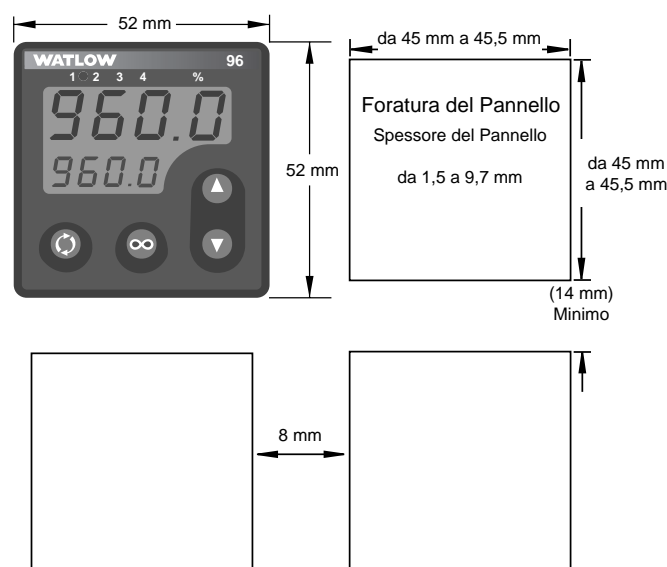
Dimensioni di foratura del pannello multiplo della Serie 96.
